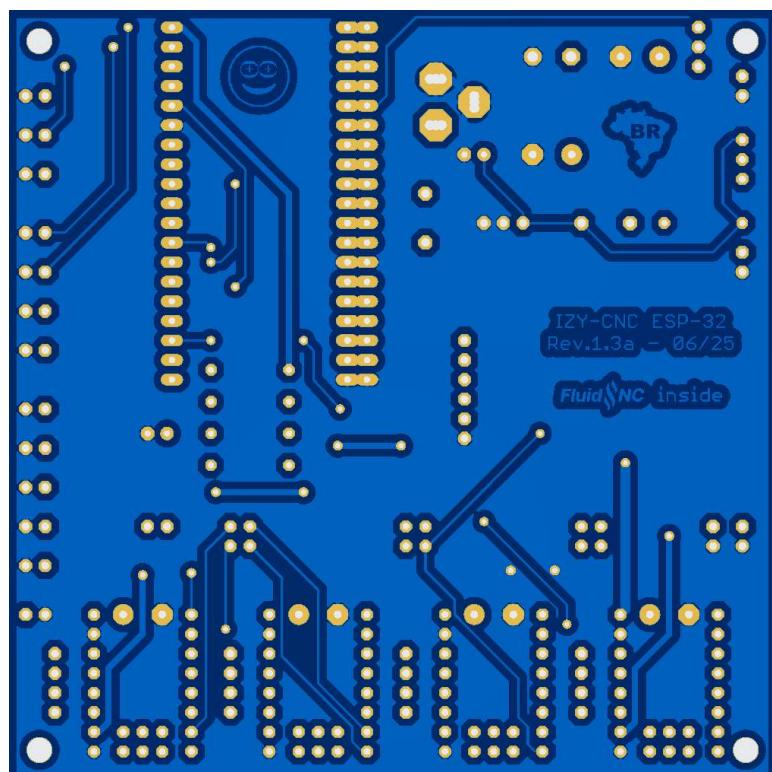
Placa IZY-CNC - Rev.1.3a (VG) – Lado da solda
